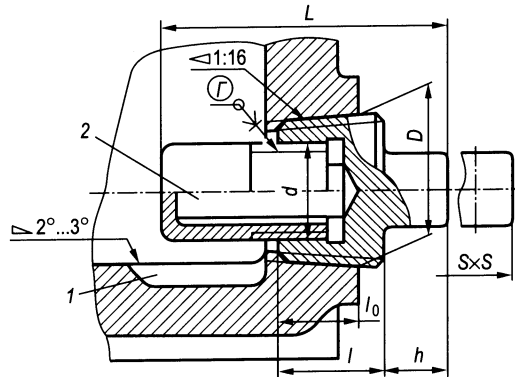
Магнитная пробка с конической резьбой для маслоспускного отверстия:
